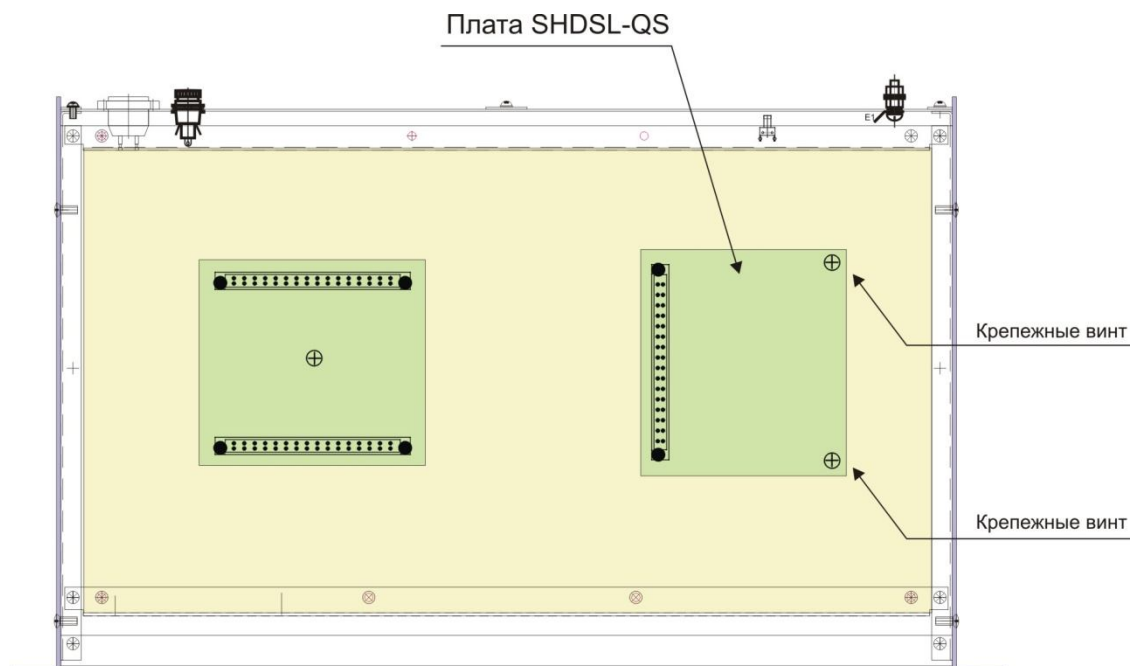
Внешний вид устройства со снятой верхней крышкой
